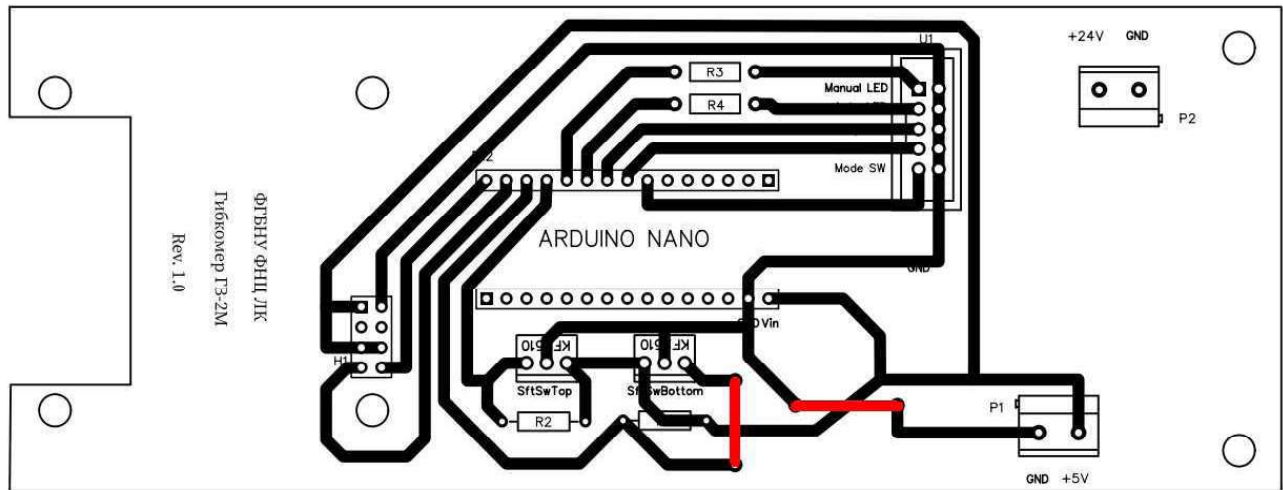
Внешний вид печатной платы гибкомера ГВ-2М
